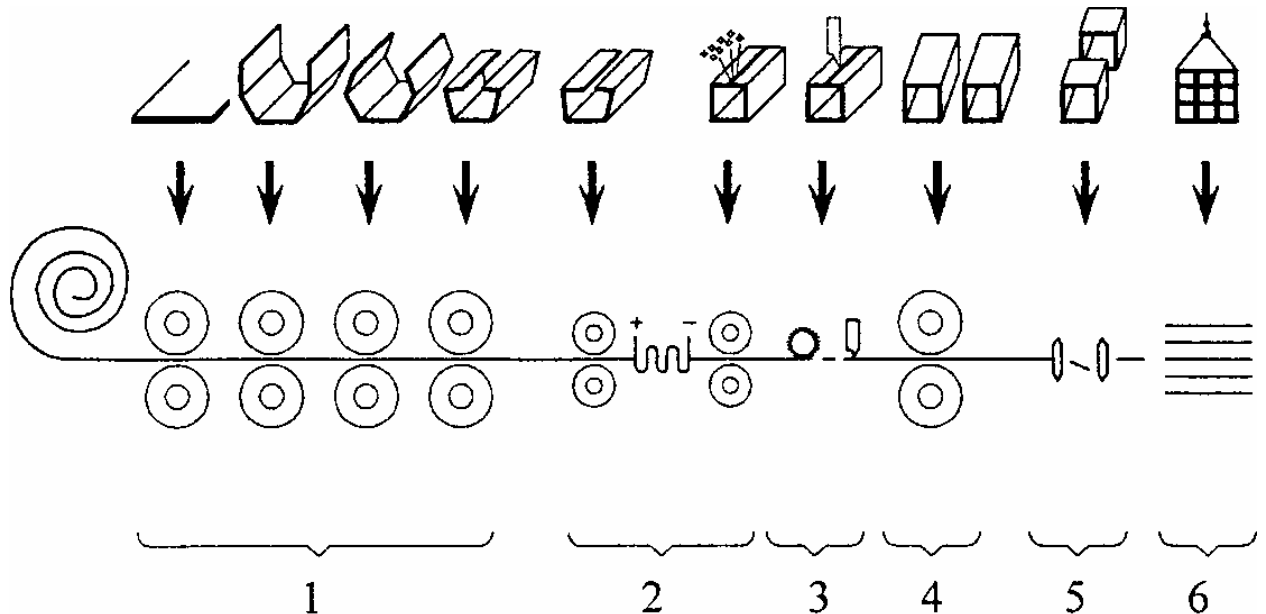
Схема виготовлення гнutoзварних замкнених профілів: 1 - профілювання; 2 - зварювання струмом високої частоти; 3 - зняття ґрату; 4 - правка; 5 - відрізка; 6 - пакетування
